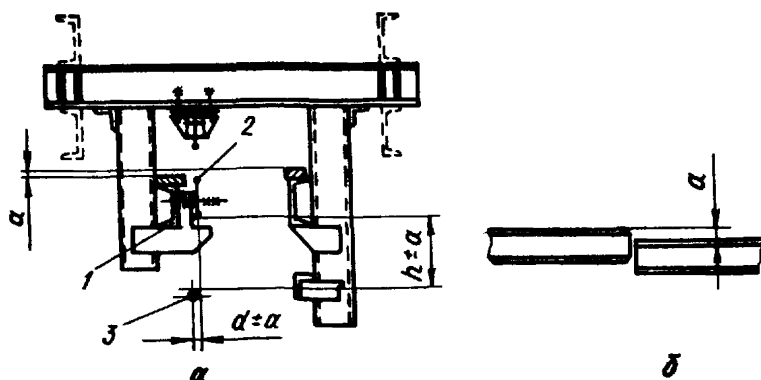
Допуски на установку выключателя (выключателя);
